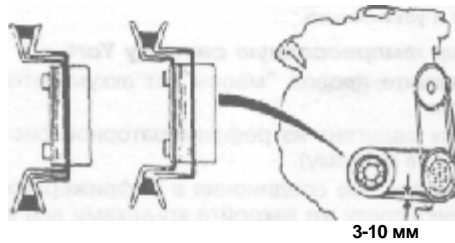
Регулировка приводного ремня компрессора — компрессорная система York
